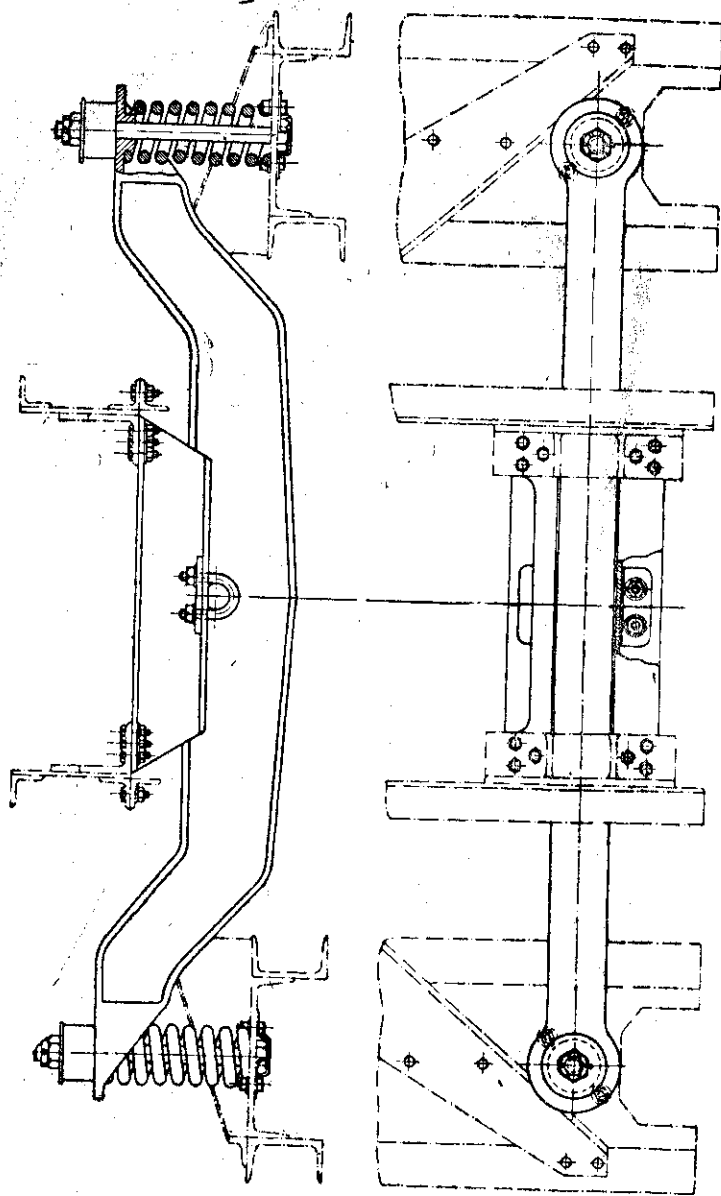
Схема полужесткой подвески (рама катков опирается на корпус через ось ведущего колеса).
